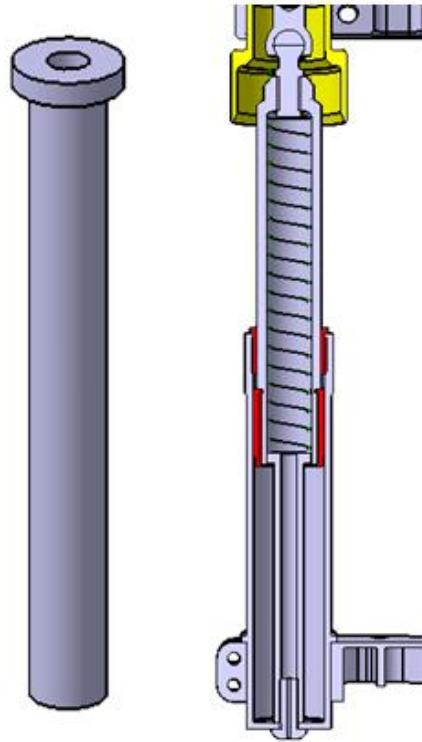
Pieza MT2-DI-00-08 (izda.). Montaje final de la pieza MT2-DO-00-08 (dcha.).
